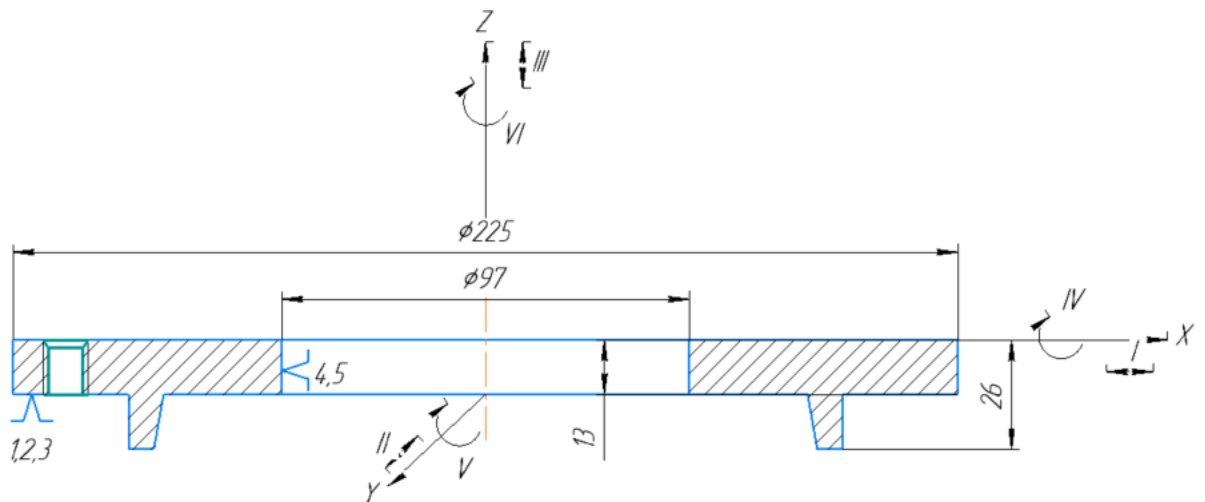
Схема установки заготовки в 3х кулачковий патрон за торець 225 і отвір діаметром 97
